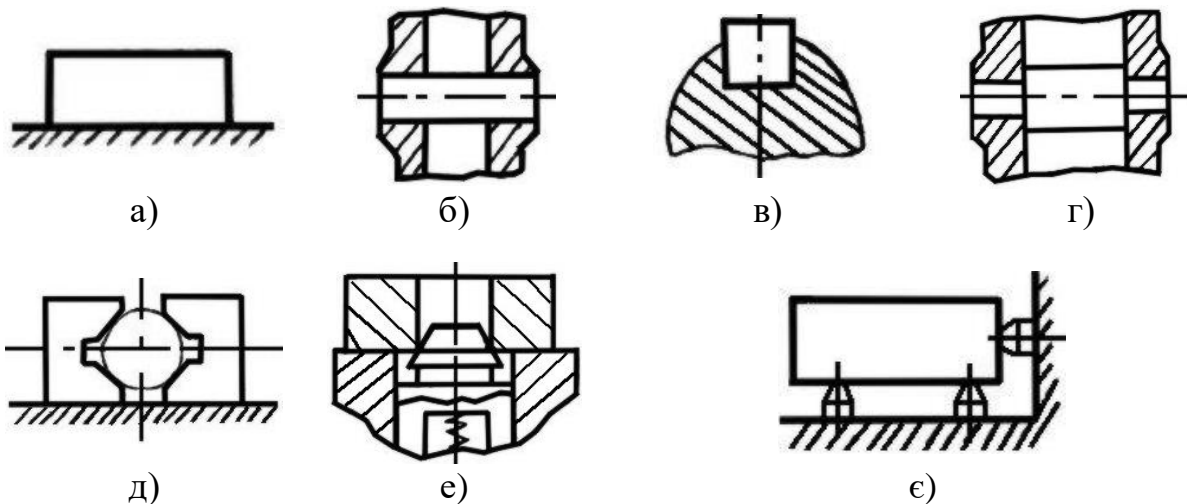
Види баз: а – площина; б – циліндр; в, г – сукупність поверхонь; д – вісь; е – коло; ж – точка
